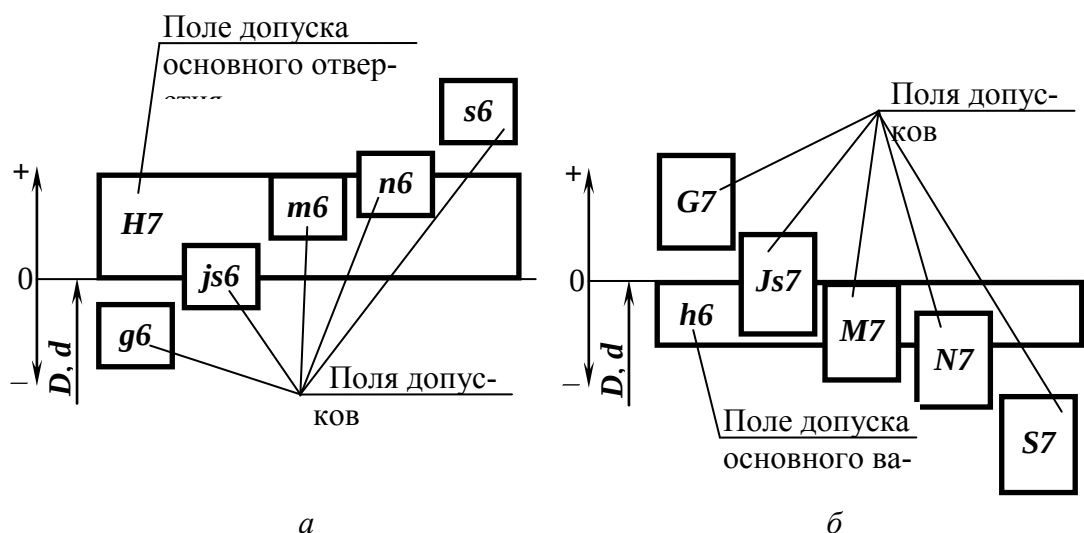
Схемы расположения полей допусков отверстий и валов:
